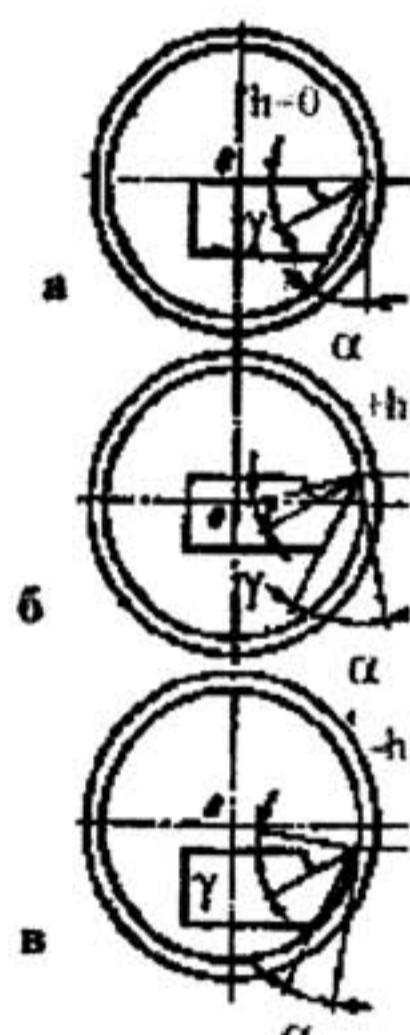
Углы α и γ при установке расточного резца относительно оси заготовки:
